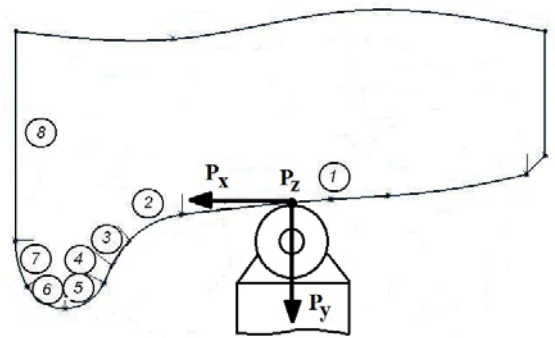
Розрахункова схема для визначення напружено-деформованого стану збірного чашкового різця в залежності від ділянки обробки колісної пари
